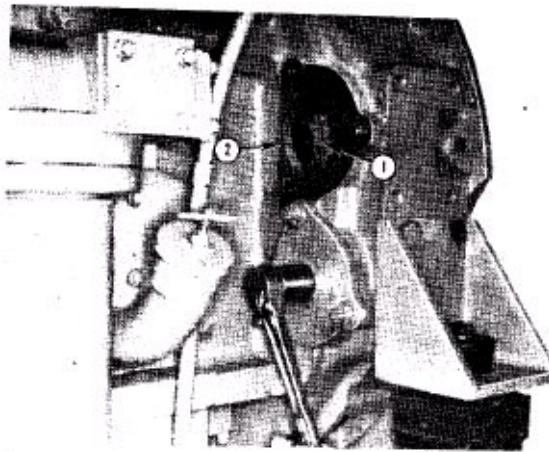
(K21919) Валоповоротный механизм двигателя.
